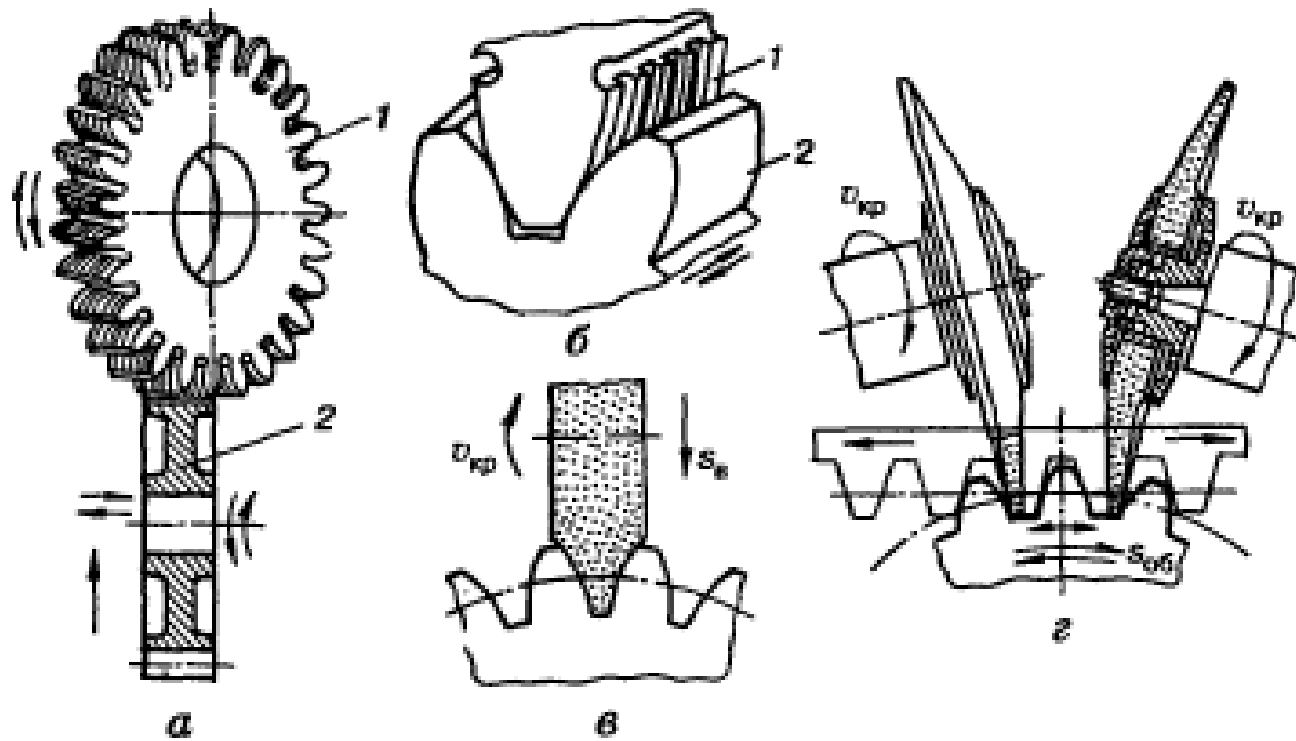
Чистова обробка зубців зубчастих коліс
